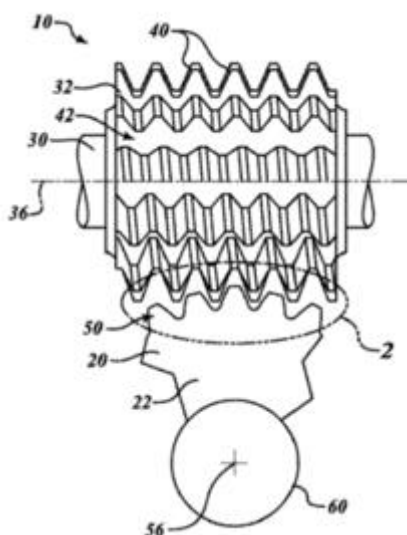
Червячная фреза и формирование зубьев в заготовке зубчатого колеса
